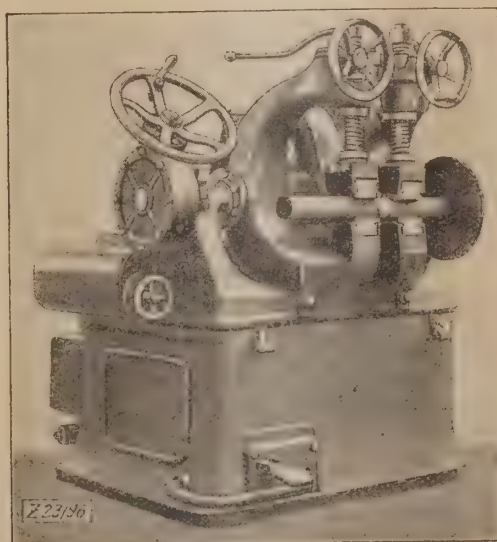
Stumpfschweißmaschine der Deutschen
